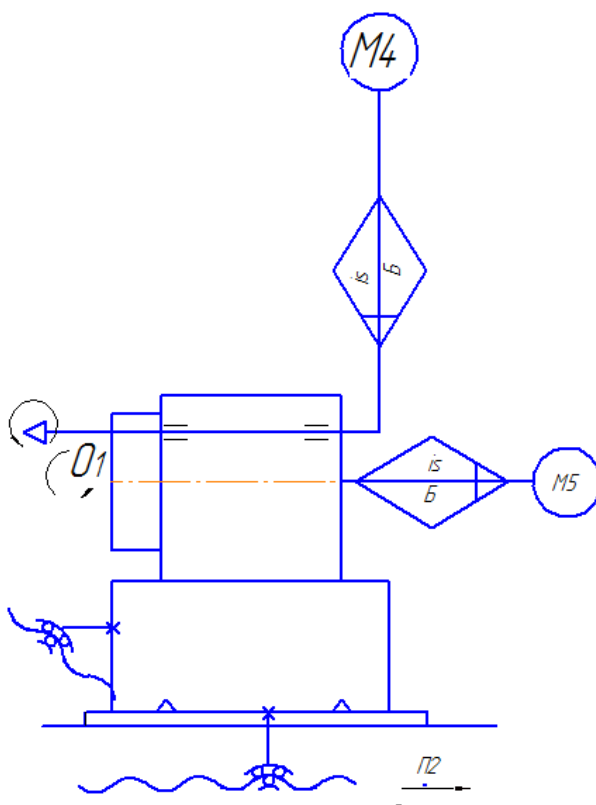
КЛ приводу обертового руху інструменту в РГ
